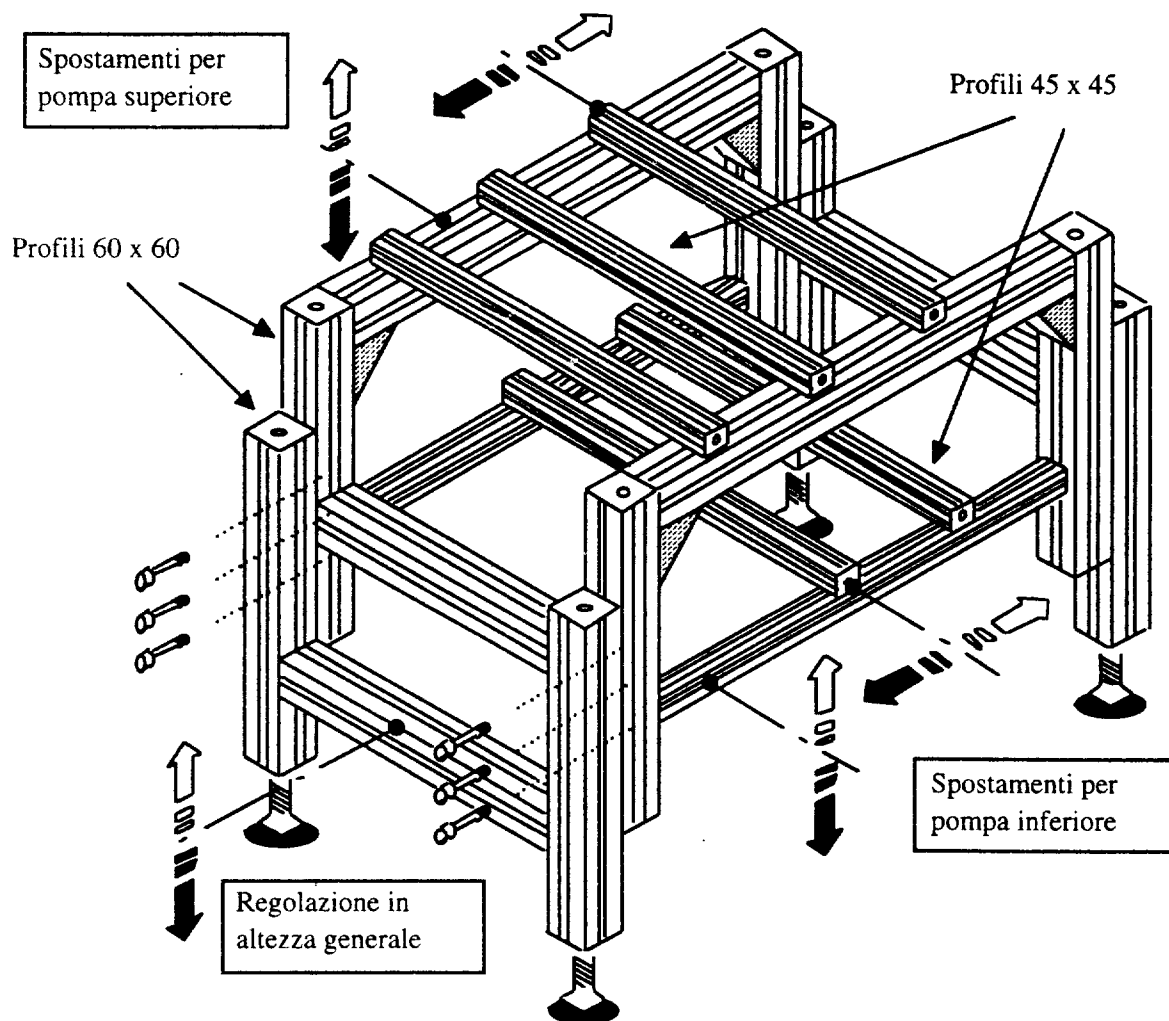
Progetto per il castelletto del gruppo pompe per il vuoto d'isolamento d'AURIGA.
